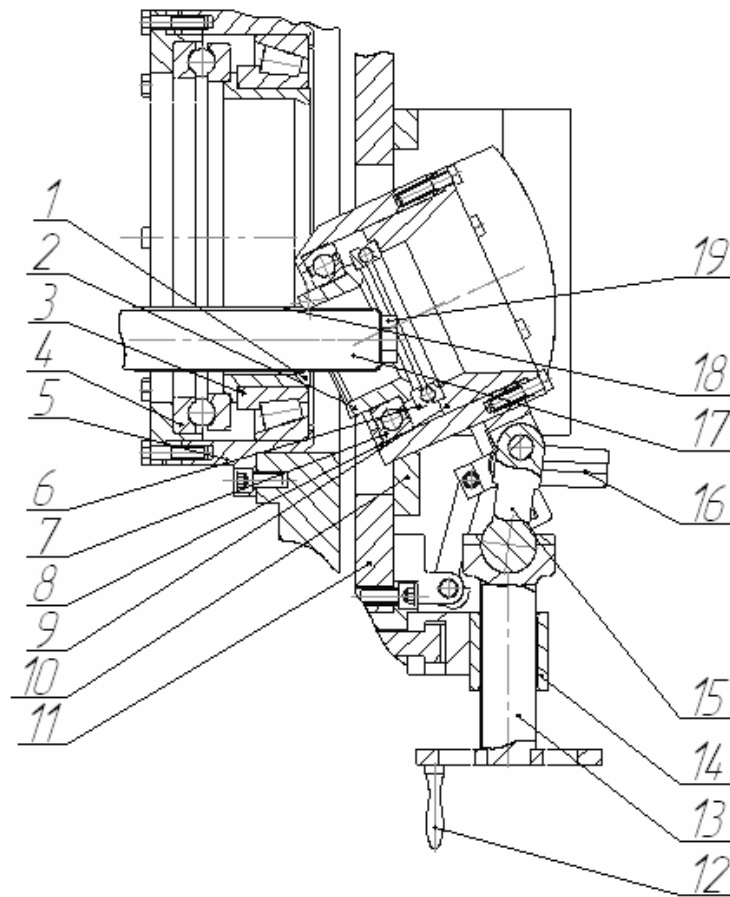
Креслення пристрою для витягування особливо тонкостінних трубчастих виробів. Поперечний переріз
